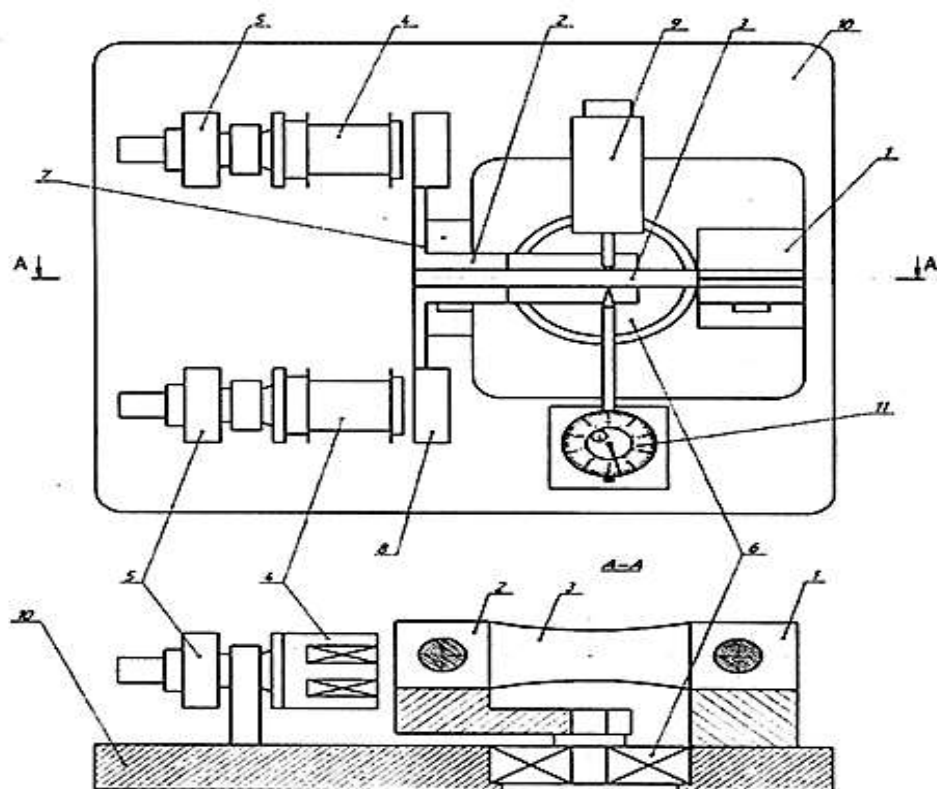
Модернизированная усталостная установка ЭМУ-5: 1 - неподвижный захват, 2 - подвижный захват, 3 - образец, 4 - электромагниты, 5 - винтовые механизмы, 6 - подшипниковый узел, 7 - реверса, 8 - якорь, 9 - индукционный датчик, 10 - основание, 11 - индикатор часового типа
